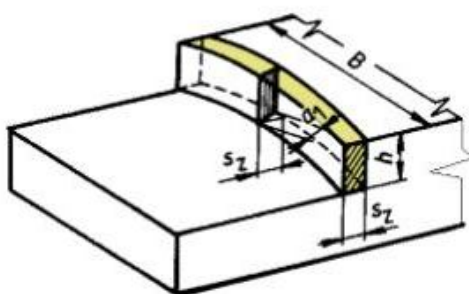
Frézovanie čelnou valcovou frézou [2]
